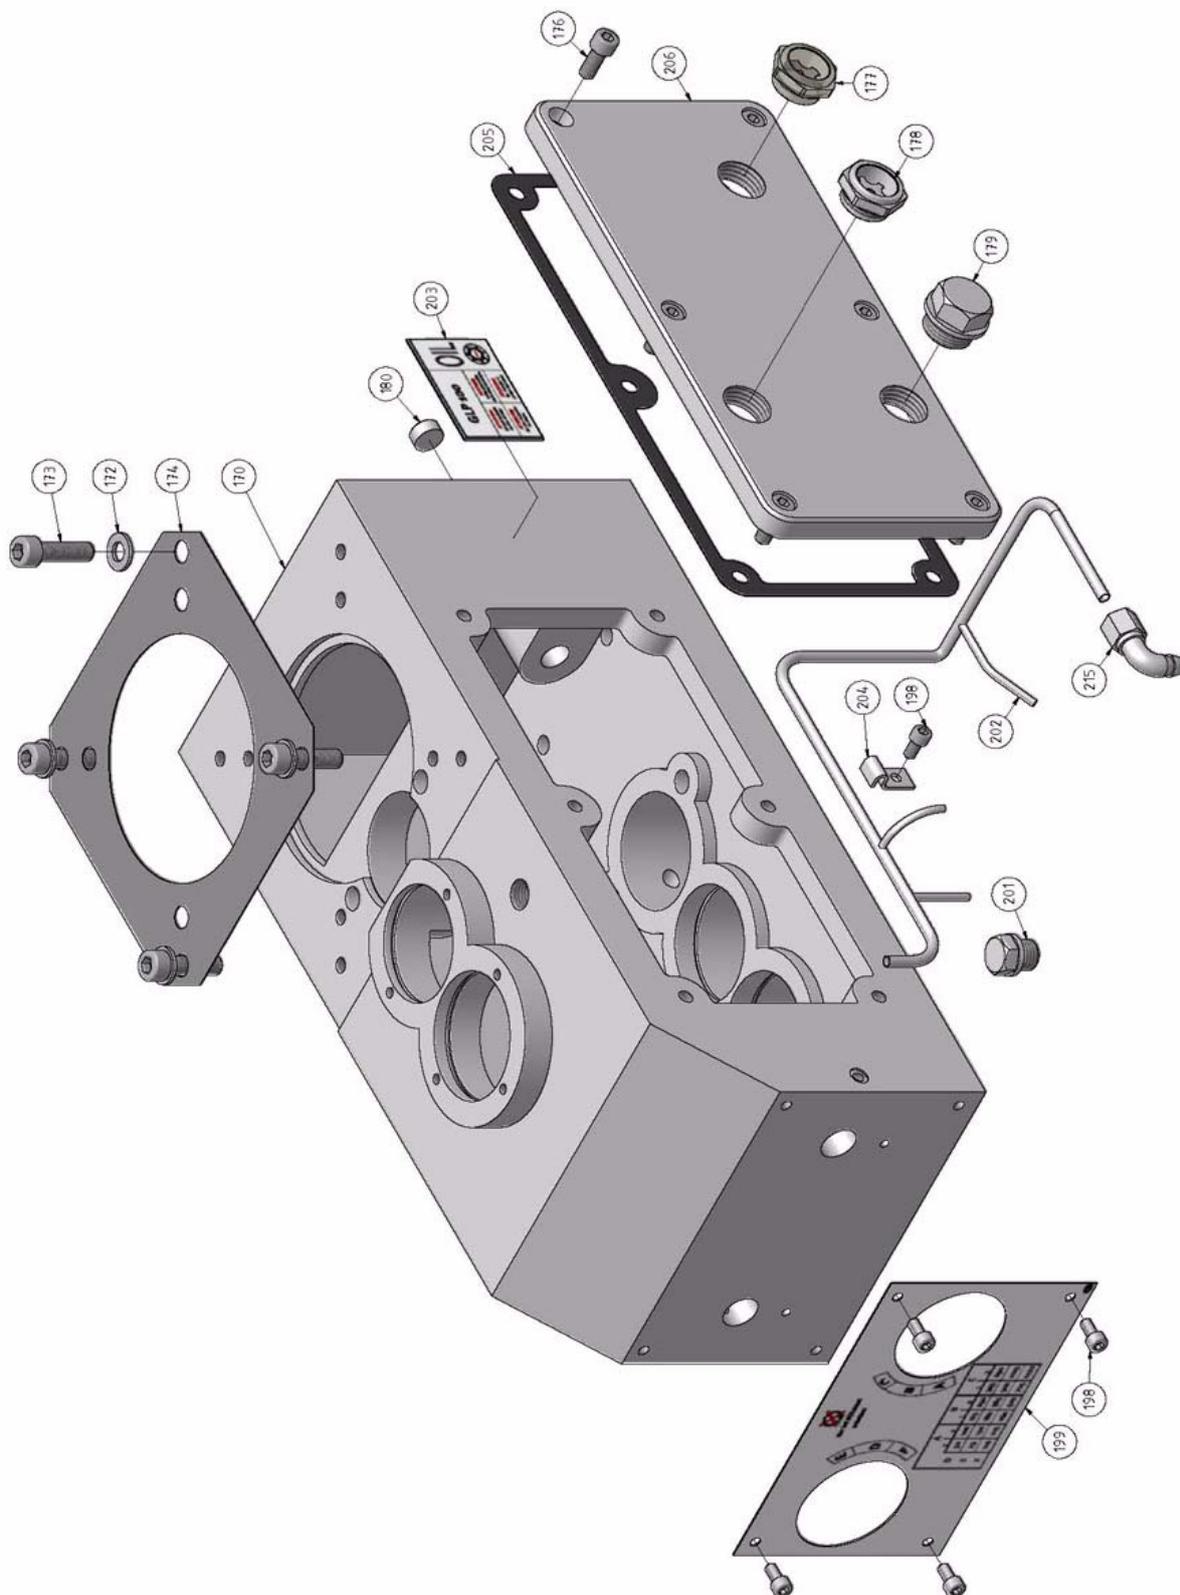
Getriebe Bohrspindel 4 von 4 - Gear box main spindle 4 von 4
